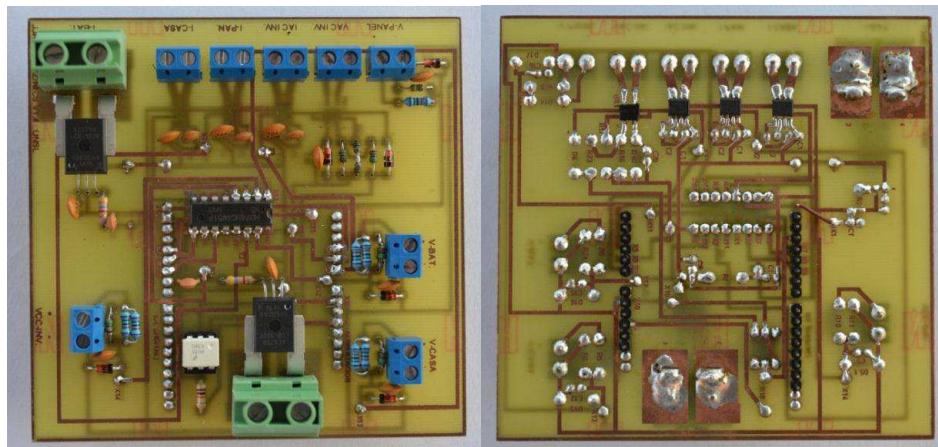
(Izq.) Lado TOP placa. (Dcha.) Lado BOTTOM Placa.
